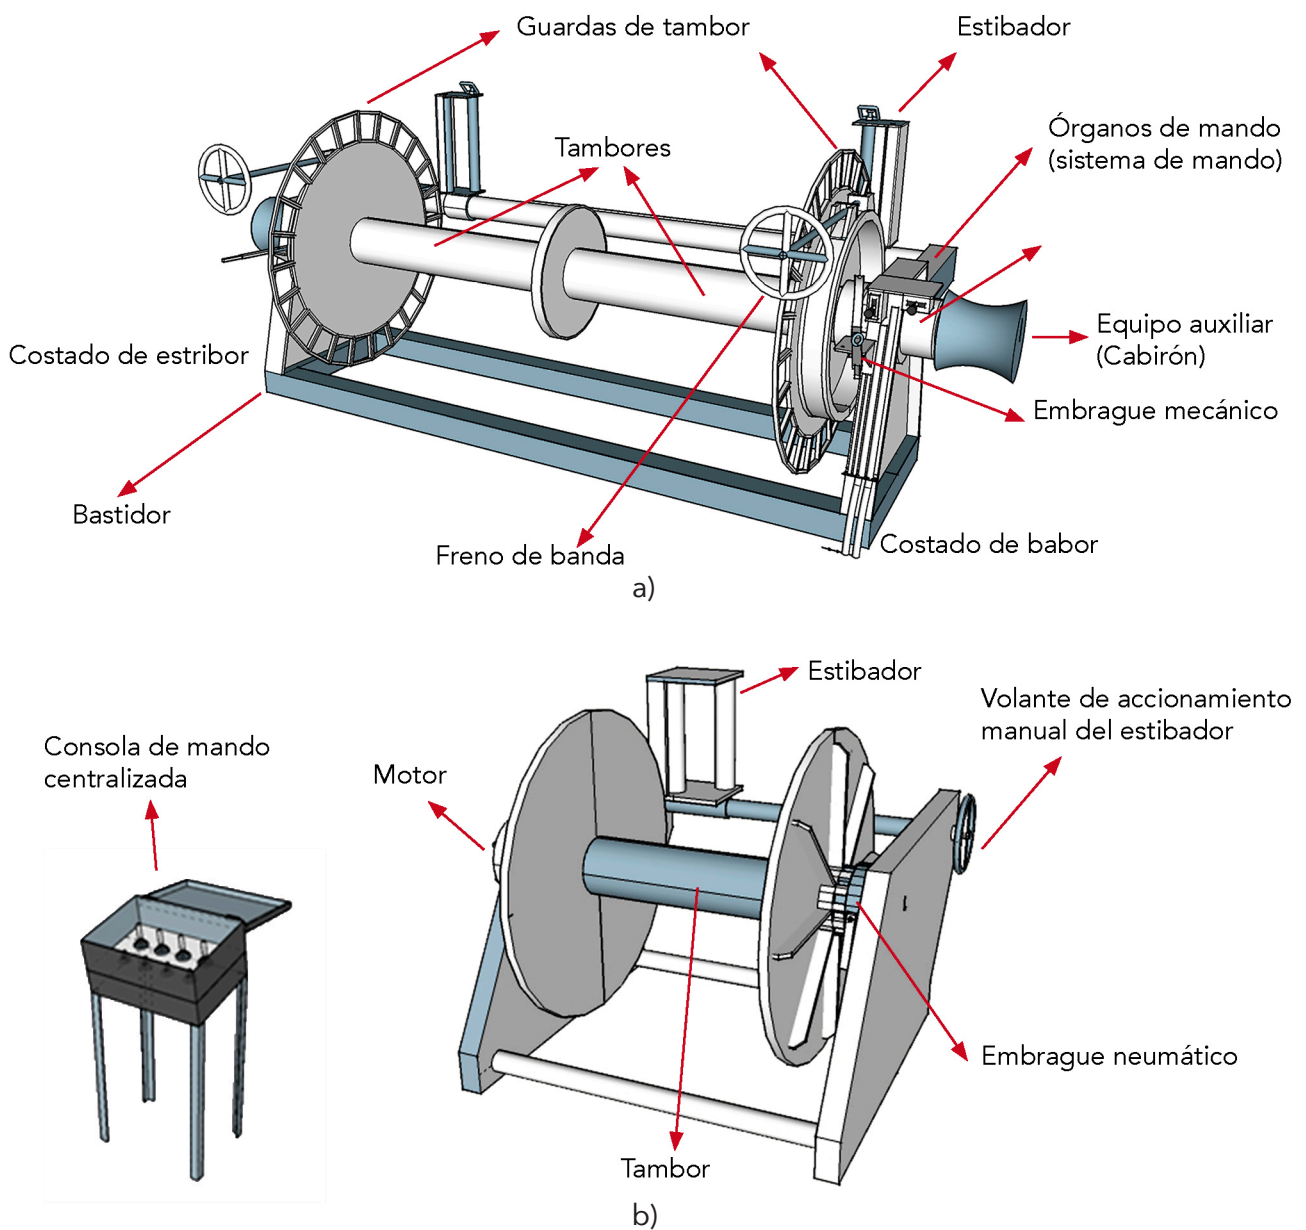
Partes de una maquinilla. a) Maquinilla tipo monobloque para cable, malleta y red (vista desde la parte anterior). b) Maquinilla tipo partida para cable o cable y malleta (vista desde la parte anterior).
